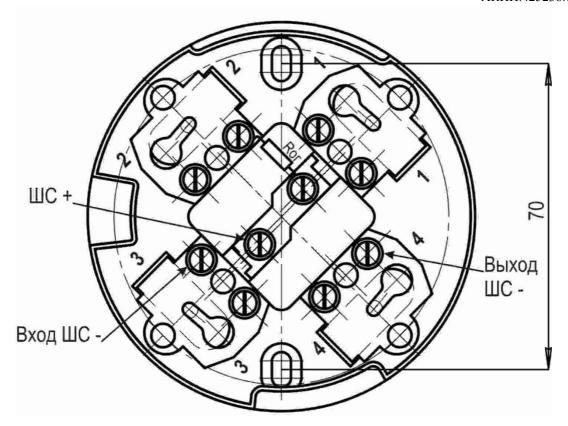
Розетка извещателя. Общий вид и расположение контактов
